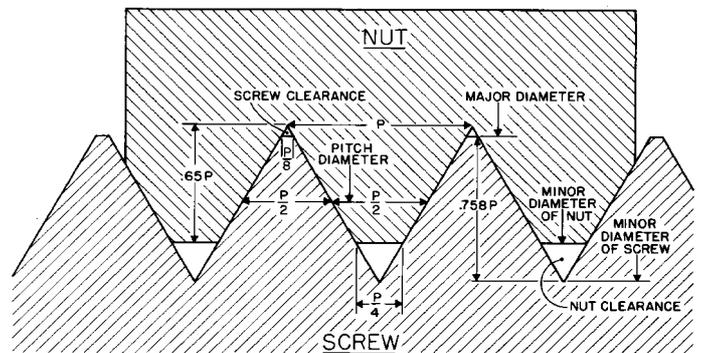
Die verschiedenen Teile eines Gewindes, das mit einem 60° Gewindestahl geschnitten wurde
